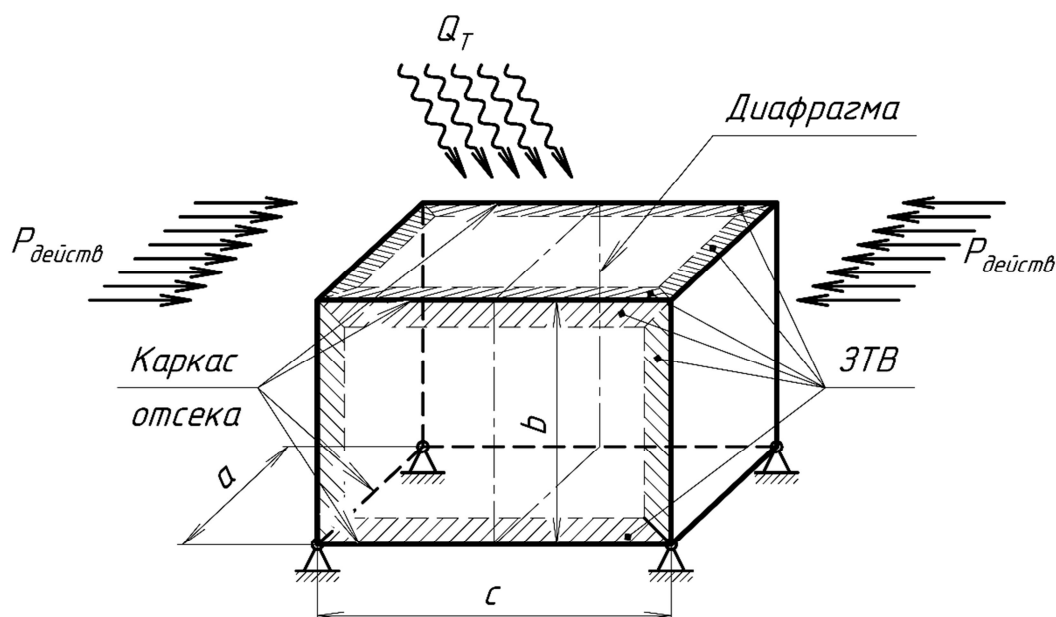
Расчетная схема обобщенного сварного отсека и нагружения его верхней панели
